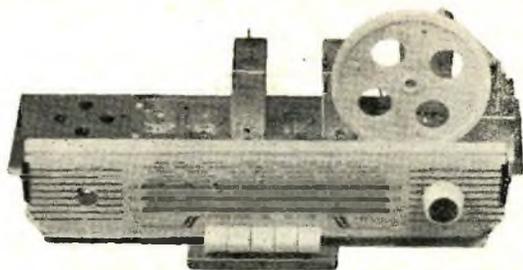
Come si presenta il telaio a montaggio di alcuni componenti.
